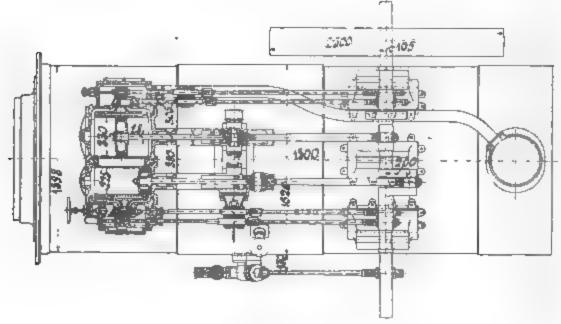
1759. Kompoundlokomobile. Heisfläche 40 qm, Dampfdruck 8 Atm., Maschine 225/330, Hub 400, Umdrehungen 130.
